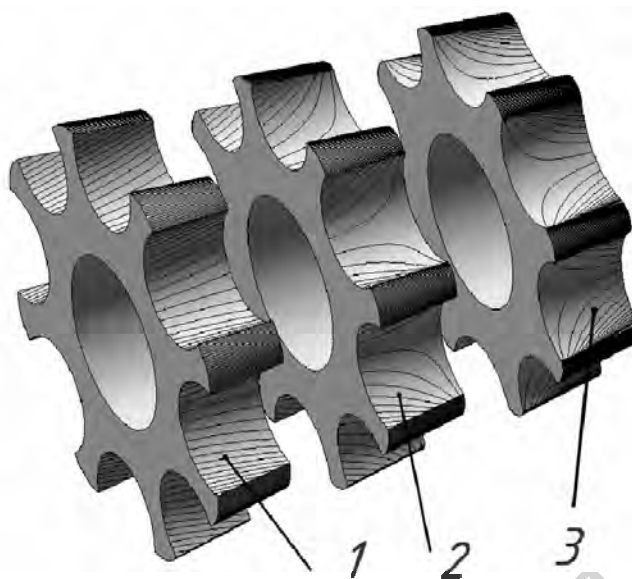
Сателлитное колесо прецессионной роликовой передачи с широким зубчатым венцом
